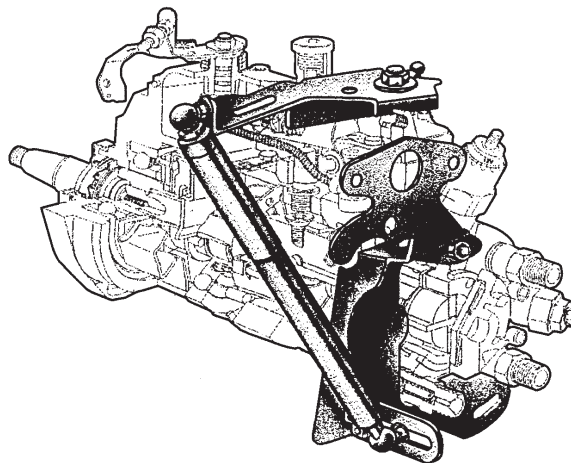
Расположение демпфера рычага управления на корпусе ТНВД.
